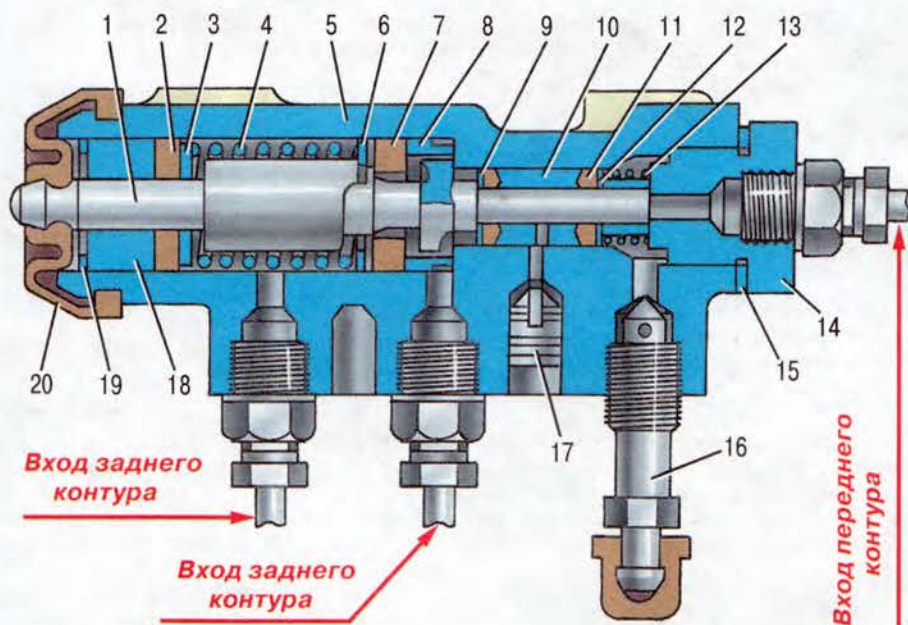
Регулятор давления: 1 – поршень; 2 – уплотнительное кольцо поршня; 3, 6 – опорные шайбы пружины поршня; 4 – пружина поршня; 5 – корпус; 7 – уплотнитель головки поршня; 8 – втулка корпуса; 9 – опорная шайба втулки толкателя; 10 – втулка толкателя; 11 – уплотнительное кольцо толкателя; 12 – опорная тарелка; 13 – пружина втулки толкателя; 14 – пробка; 15 – прокладка пробки; 16 – клапан выпуска воздуха; 17 – заглушка; 18 – втулка поршня; 19 – стопорное кольцо; 20 – защитный чехол
